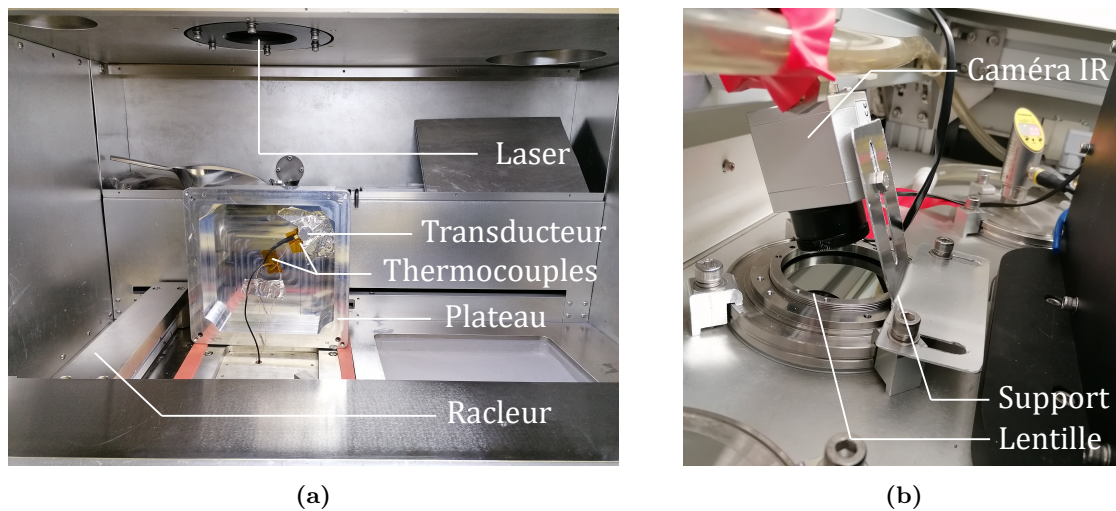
(a) Installation du plateau dans la chambre de fabrication de la machine Farsoon et (b) de la caméra thermique au-dessus de la chambre.
